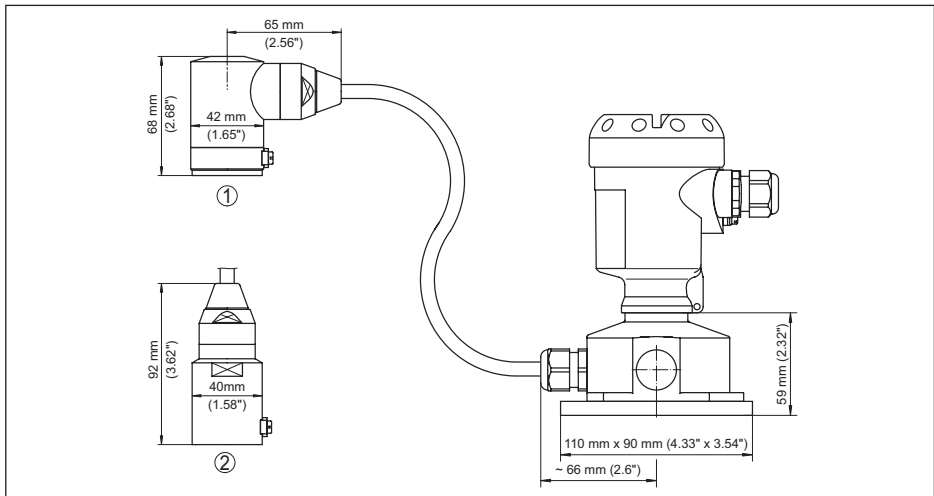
IP 68-Ausführung mit externem Gehäuse
